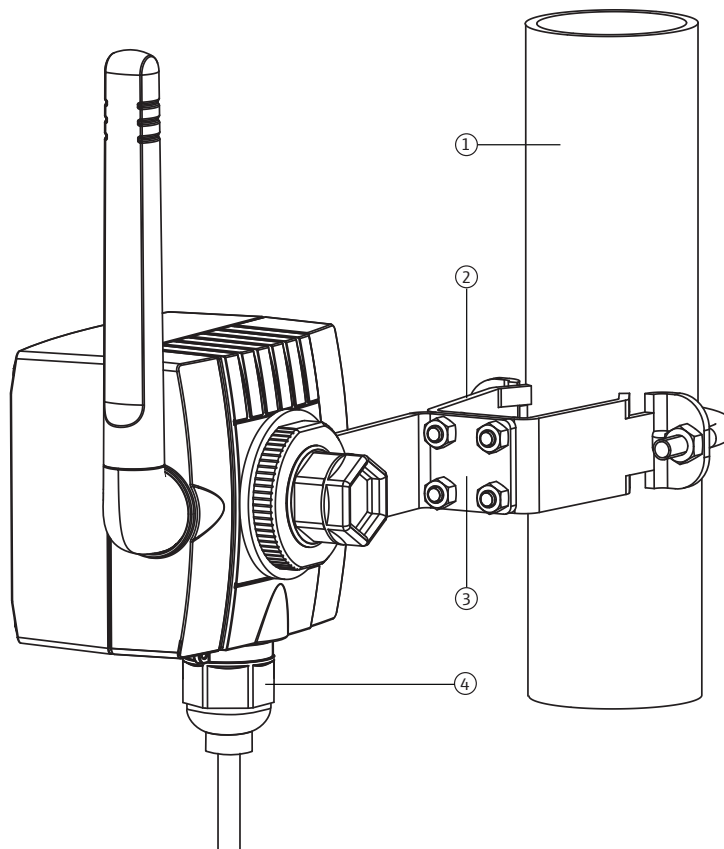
Раздельный монтаж на трубопроводе с помощью монтажного кронштейна
